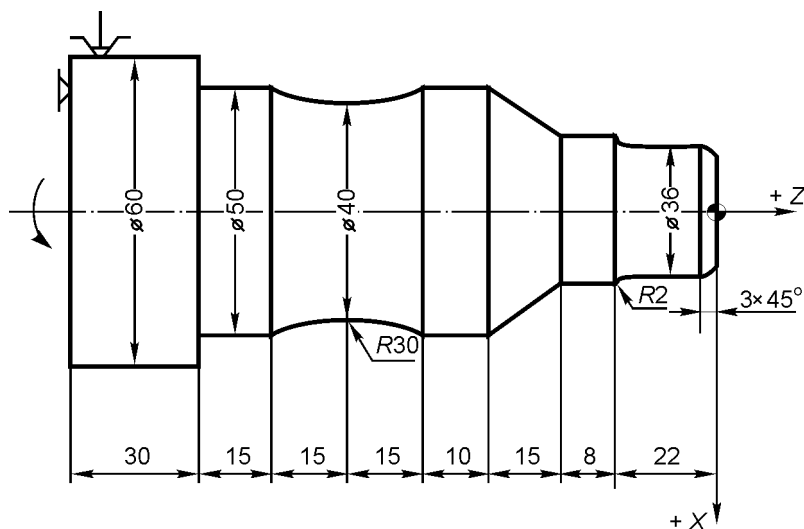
Ескіз деталі до прикладу побудови КП чистової обробки
